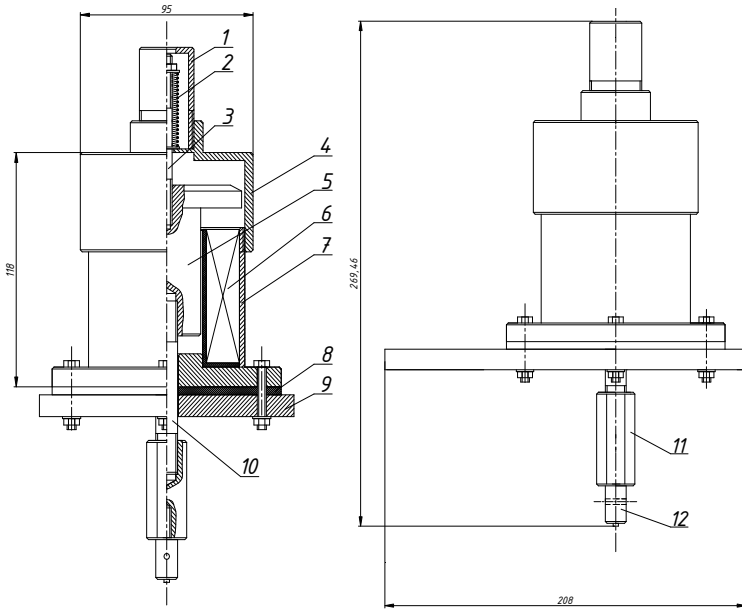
Лінійний електромагнітний двигун: 1 – кришка пружини; 2 – пружина; 3 – стрижень верхній; 4 – кришка; 5 – якір; 6 – котушка; 7 – корпус; 8-прокладка; 9 – плита верхня; 10 – стрижень нижній; 11 – перехідник; 12 – робочий інструмент
